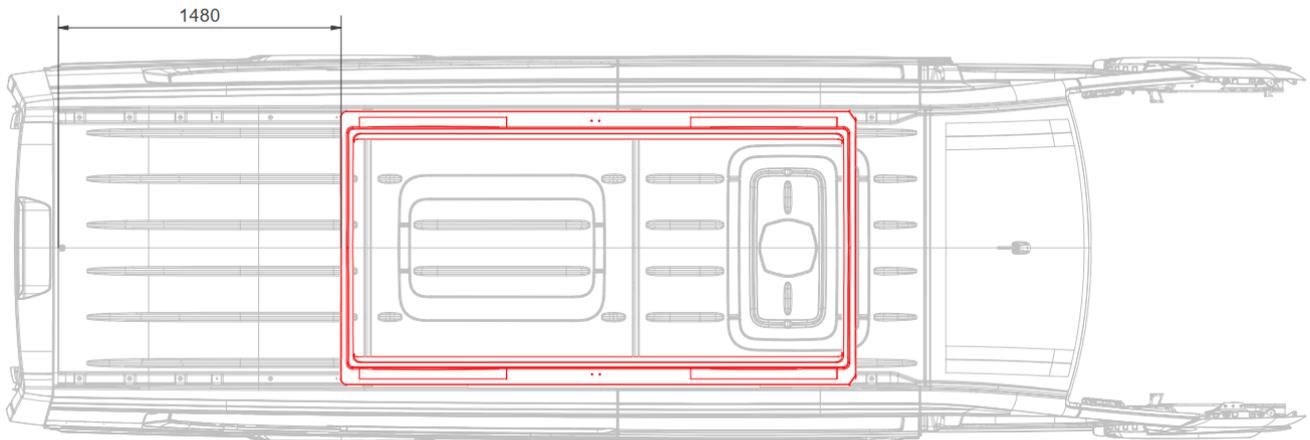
VW Crafter L5H3 (L = 7391 mm) [G0002143-001]
